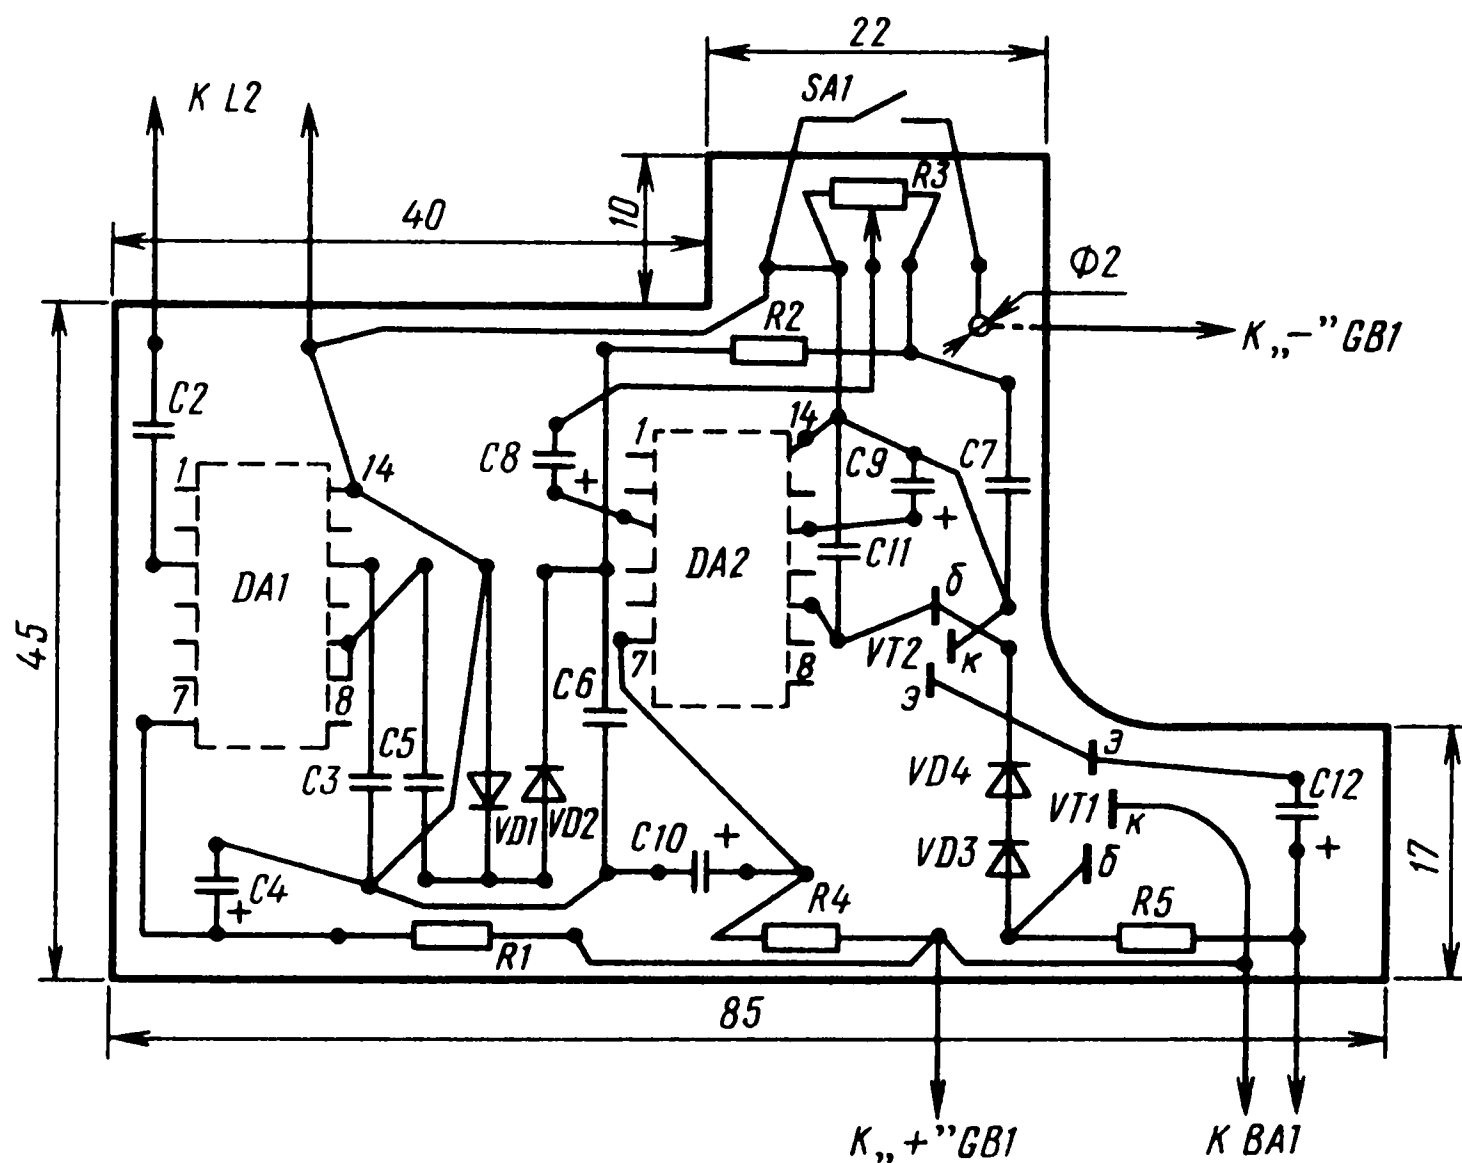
Расположение и соединение деталей на монтажной плате приемника (вид со стороны установки деталей)
